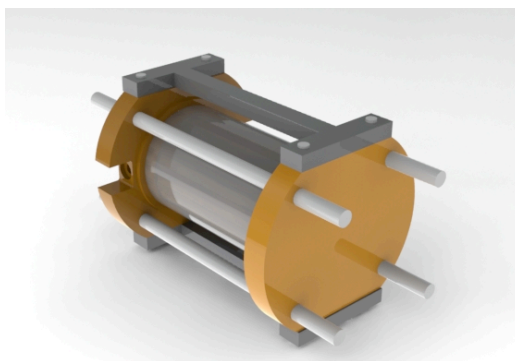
Varetas e "I"s utilizados na montagem e soldadura do interruptor para garantir o alinhamento das palhetas.
